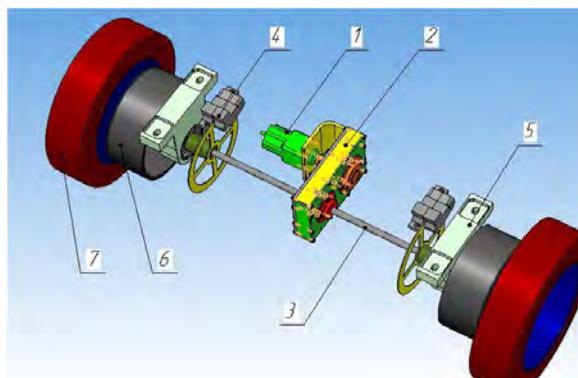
Мост управления: 1 Двигатель постоянного тока; 2 Цилиндрический редуктор; 3 Ось; 4 Тормозной механизм; 5 Опорный подшипник; 6 Опорный ролик; 7 Опорное колесо.
